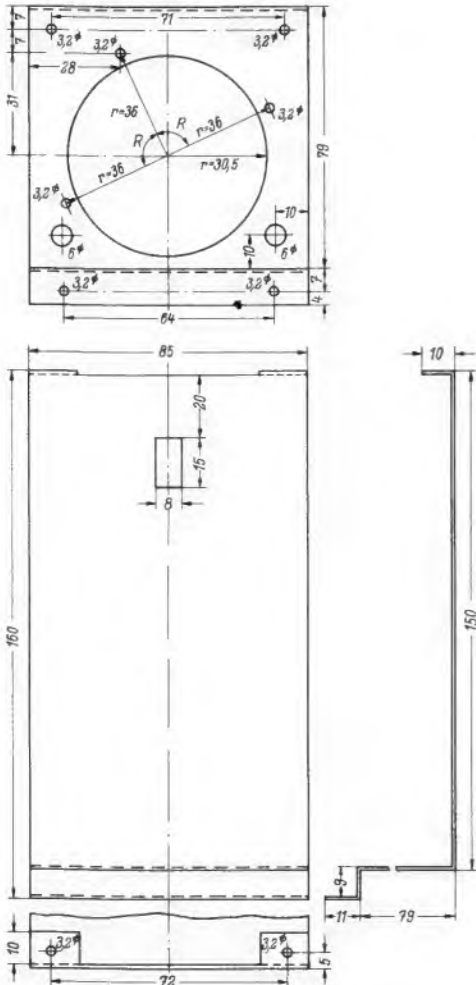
Linker Bügel für die Chassisbefestigung (Eisenblech 1mm)
